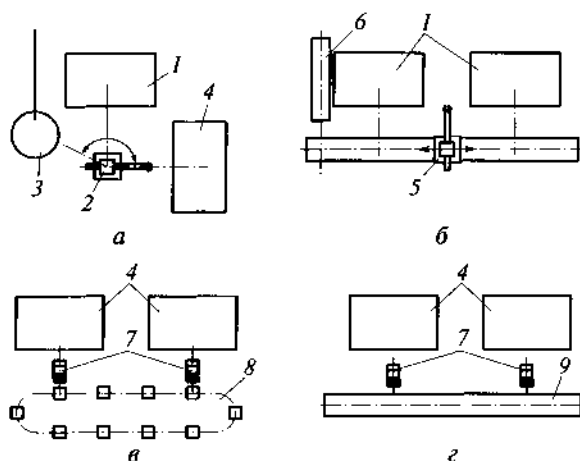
Типовые компоновки ГПМ на базе двойных станков:
